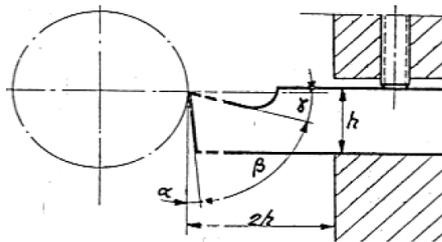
ângulos de corte Fonte - Carlos Sousa
